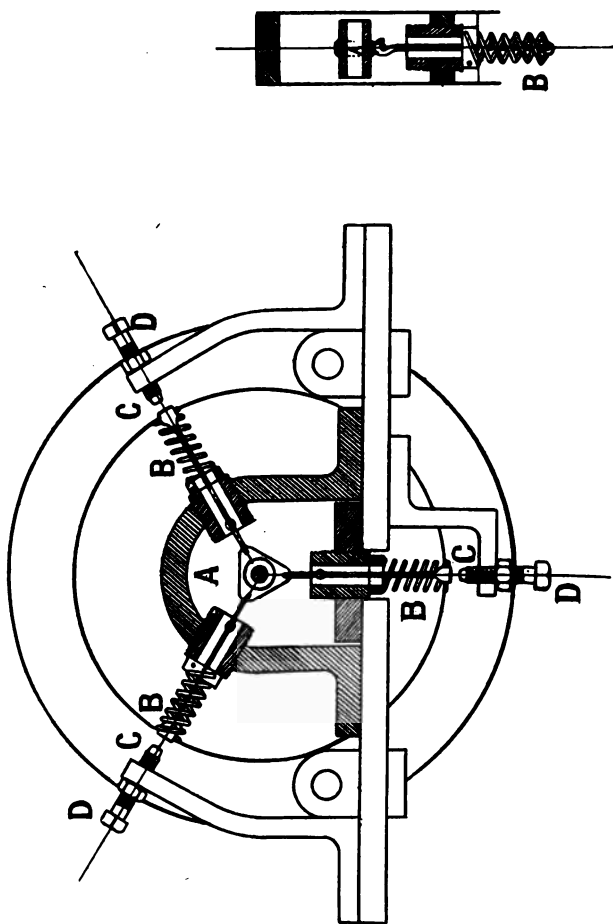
Compresseur rotatif de Maurice Leblanc. Suspension élastique du rotor.
